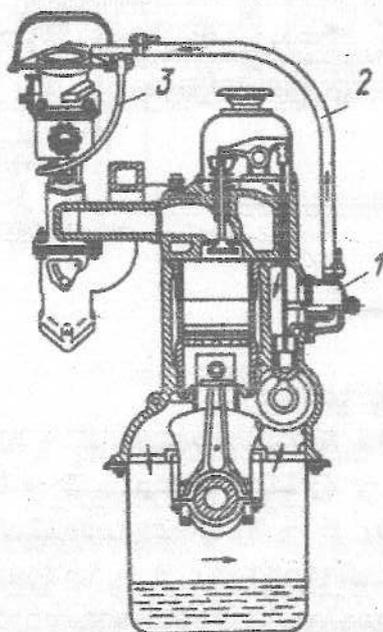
System der Kurbelgehäusebelüftung des Motors:
